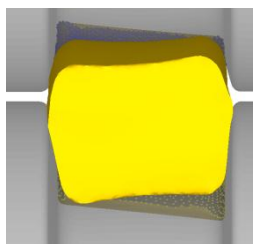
Последний момент процесса прокатки заготовки с величиной ромбичности 20 мм и начальным углом поворота заготовки  $6^\circ$
